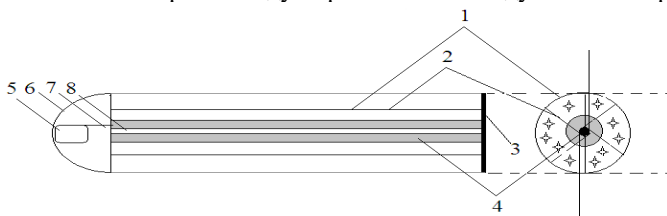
Модель контейнера з порошковим вогнегасним складом: 1 – корпус; 2 – розділювач секції; 3 – задня торцева частина контейнера; 4 – спонукальний пристрій; 5 – механізм приведення в дію спонукального пристрою; 6 – лобова частина; 7 – запальник механізму; 8 – центральна вісь
